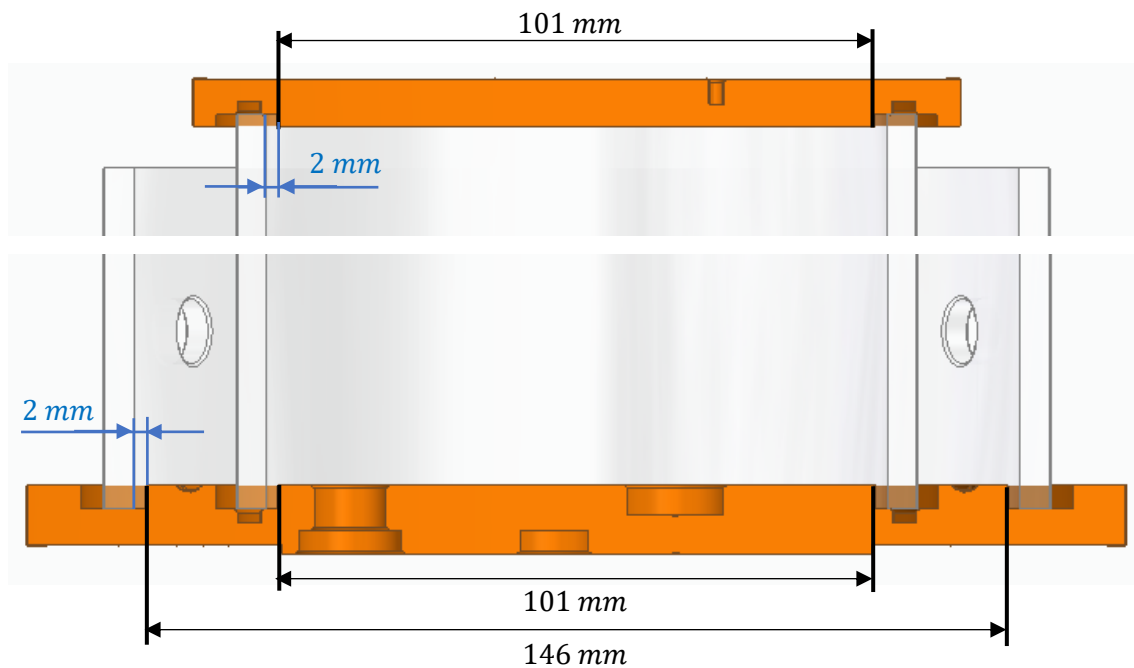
Schnittansicht von Boilerdeckel und -boden mit gewählten Innendurchmessern für die Zylinderausschnitte
